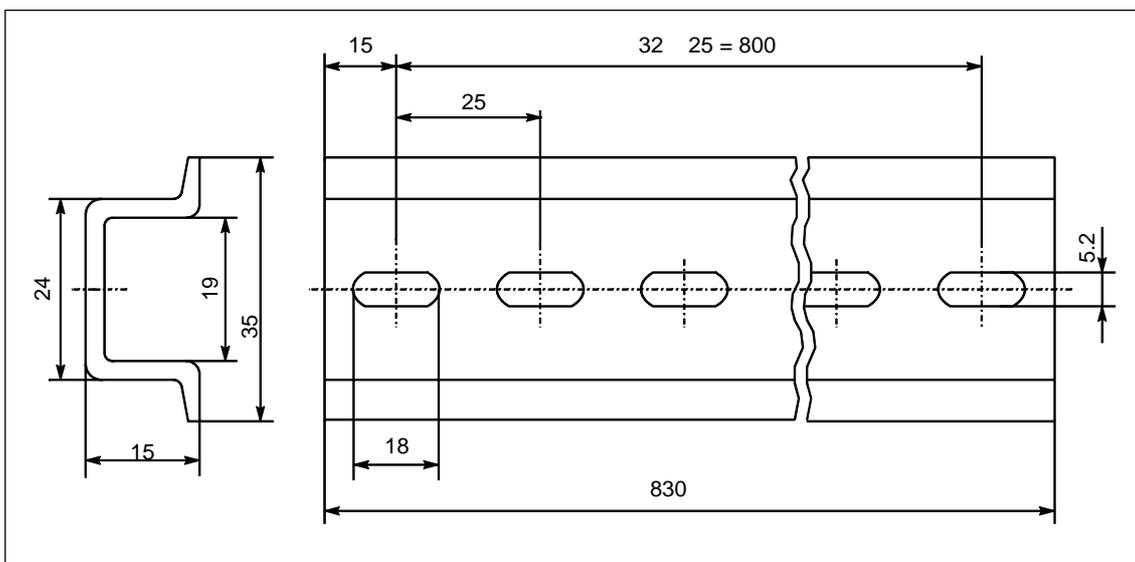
Чертеж с размерами 830-миллиметровой стандартной профильной шины
